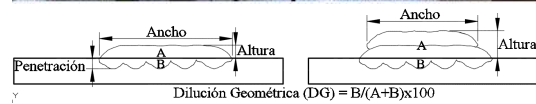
Equipos, dispositivos de soldadura y geometría de los recargues
